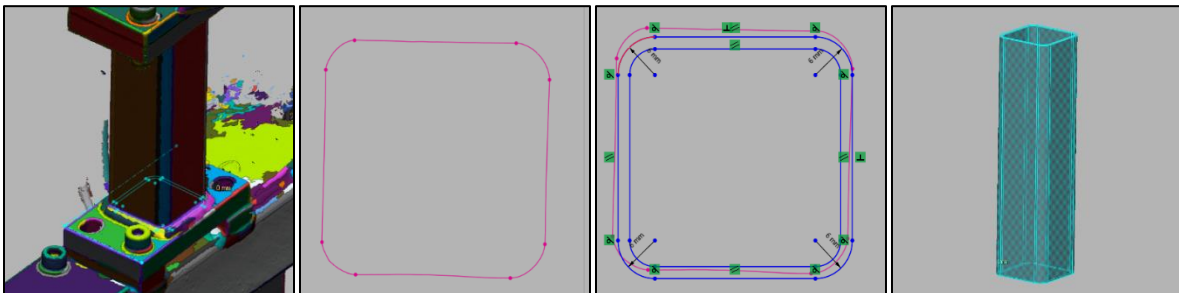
Extrusión de la pieza del elemento 1. Fuente: Desarrollo propio
